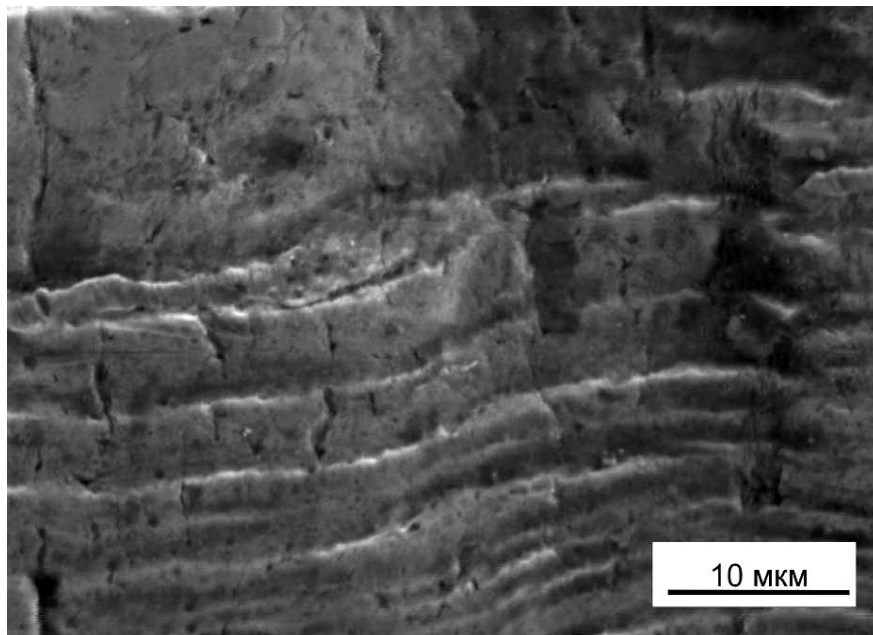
Пластически деформированные усталостные бороздки на поверхности разрушения образца. Сталь 45, закалка с отпуском при 600 °С
